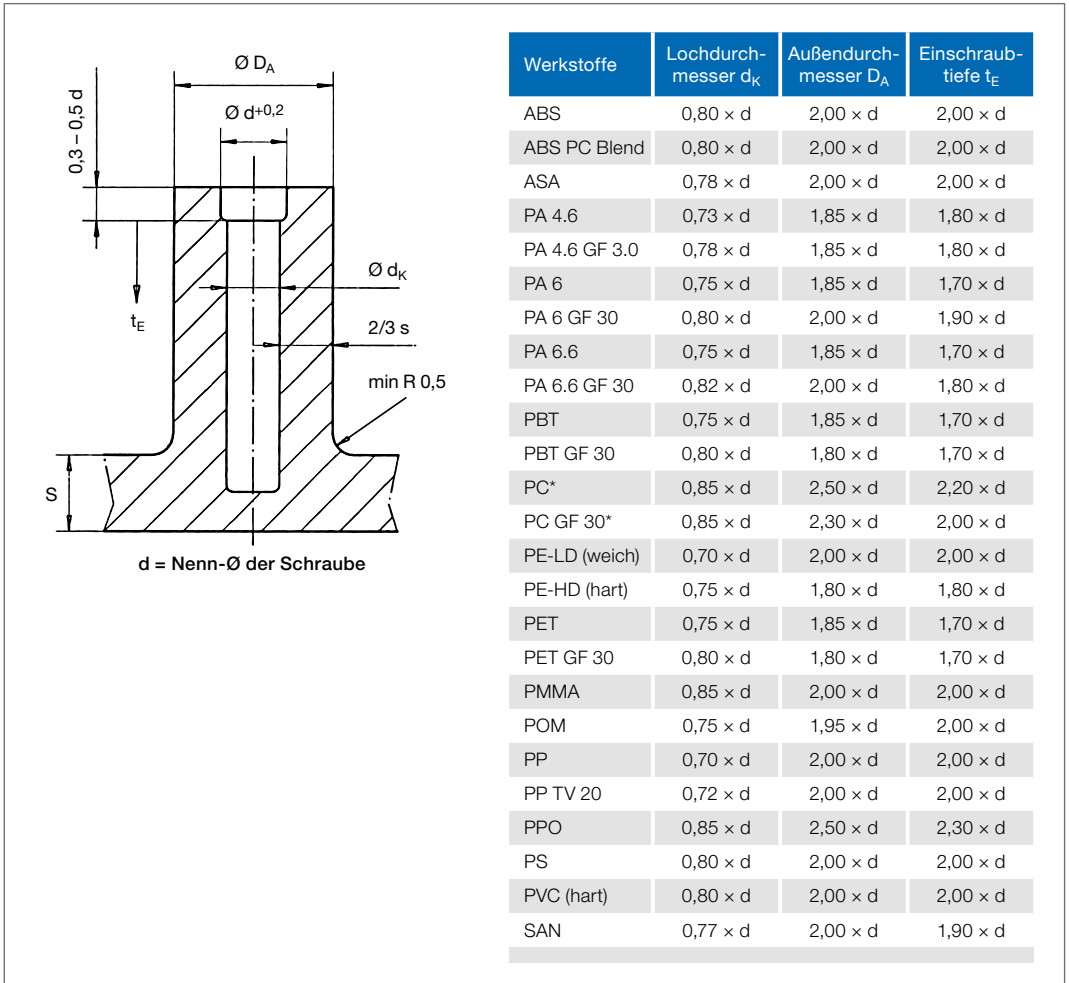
Empfohlene Tubusgestaltung für Direktverschraubungen mit AMTEC® Schrauben
